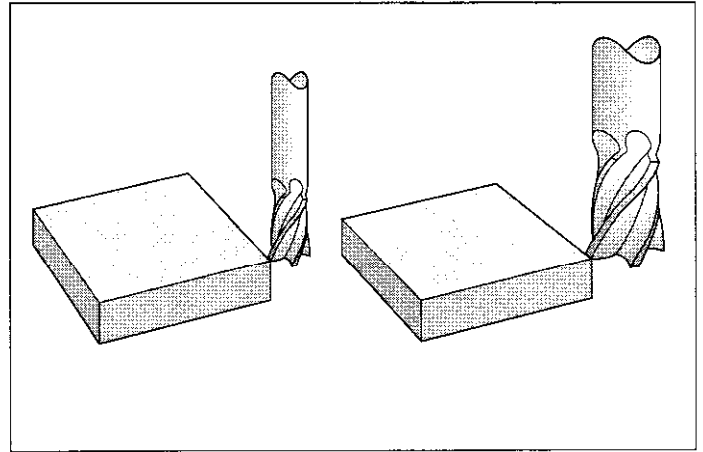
Die TNC berücksichtigt Länge und Radius des Werkzeugs
